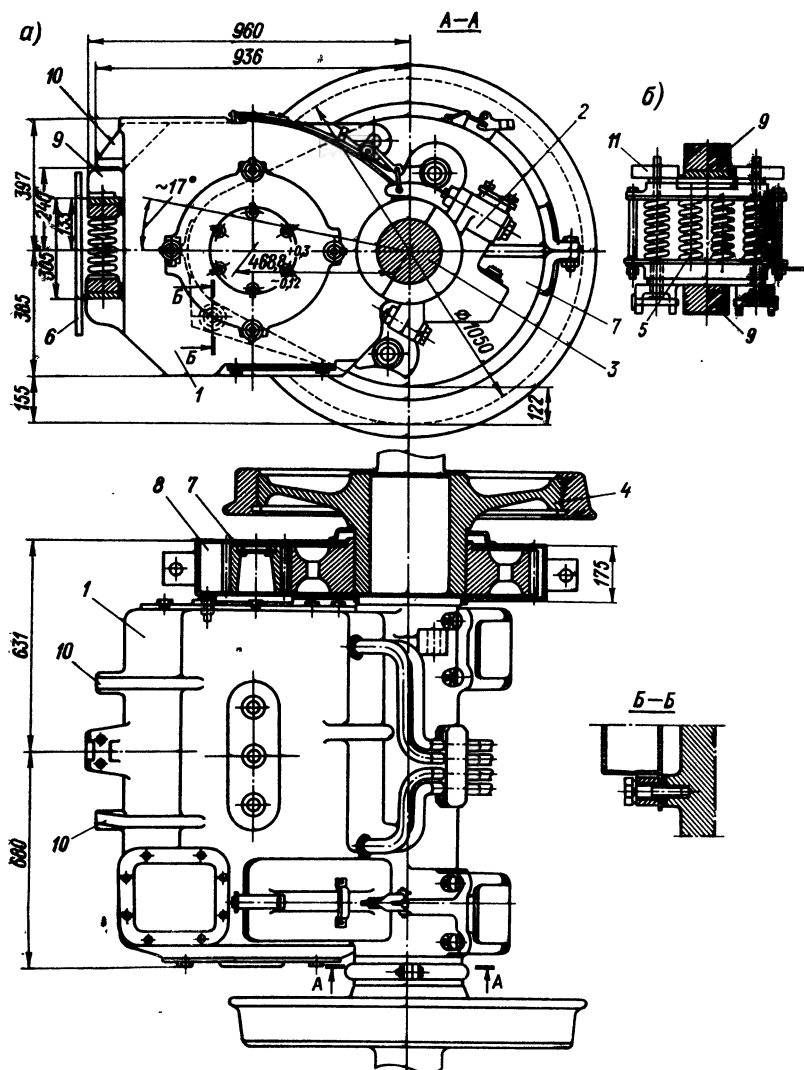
Подвесно-осевой двигатель: а — установка двигателя на колесной паре электровоза; б — подвесное пружинное устройство
